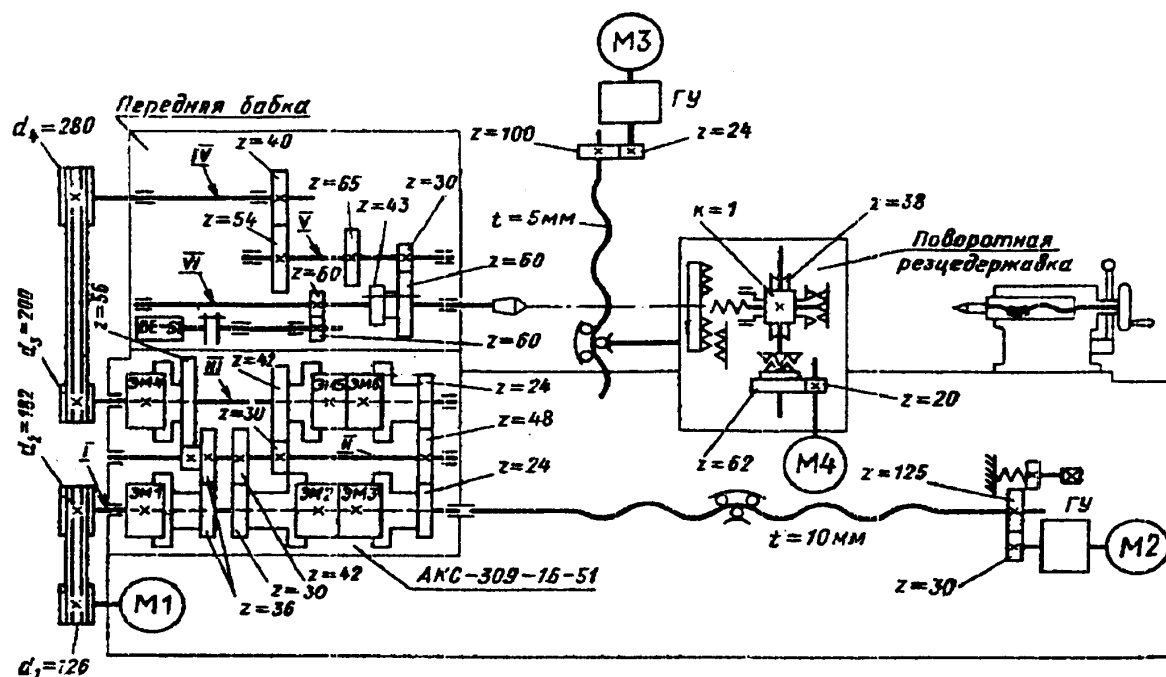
Кинематическая схема станка с ЧПУ 16К20Ф3
